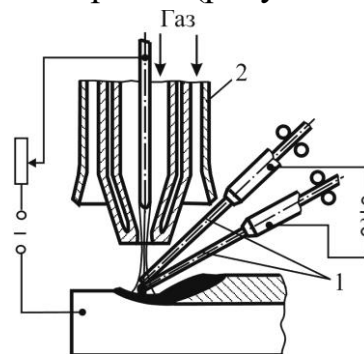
Схема плазменной наплавки с двумя присадочными проволоками
